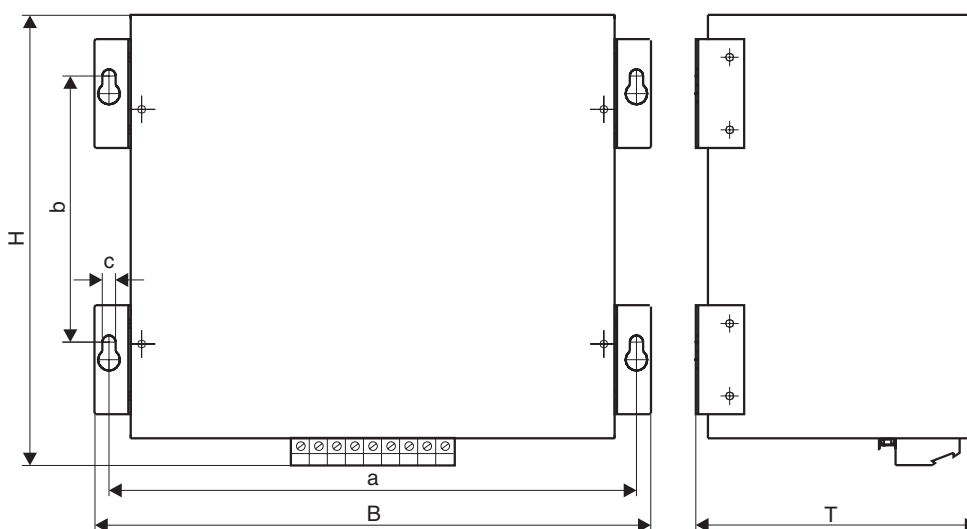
Габаритный чертеж выходных фильтров HF015...075-503
